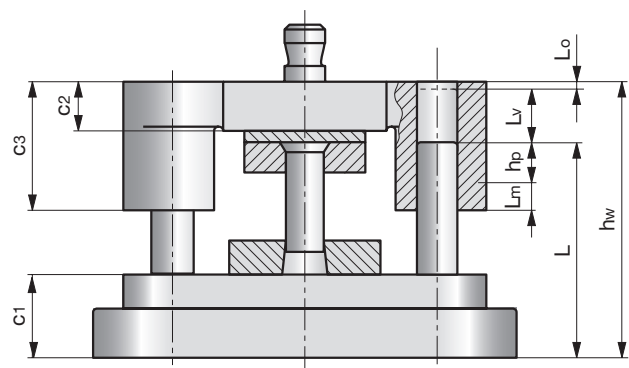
Bauhöhe „hw“ des Säulenführungswerkzeuges bei Anwendung von Einspannzapfen mit Gewindeschaft nach DIN ISO 10242-1.
